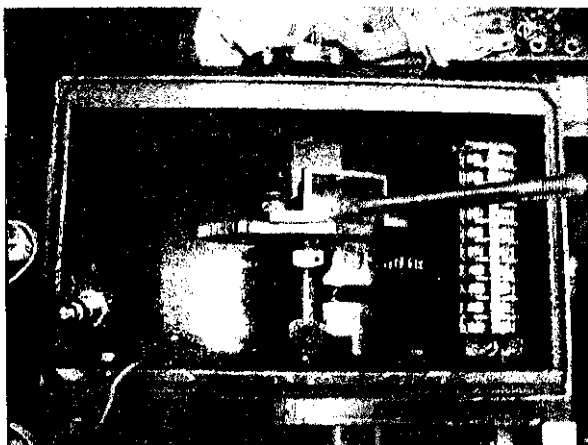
Конструкция редуктора с криволинейным кулисным механизмом для двигательного привода
